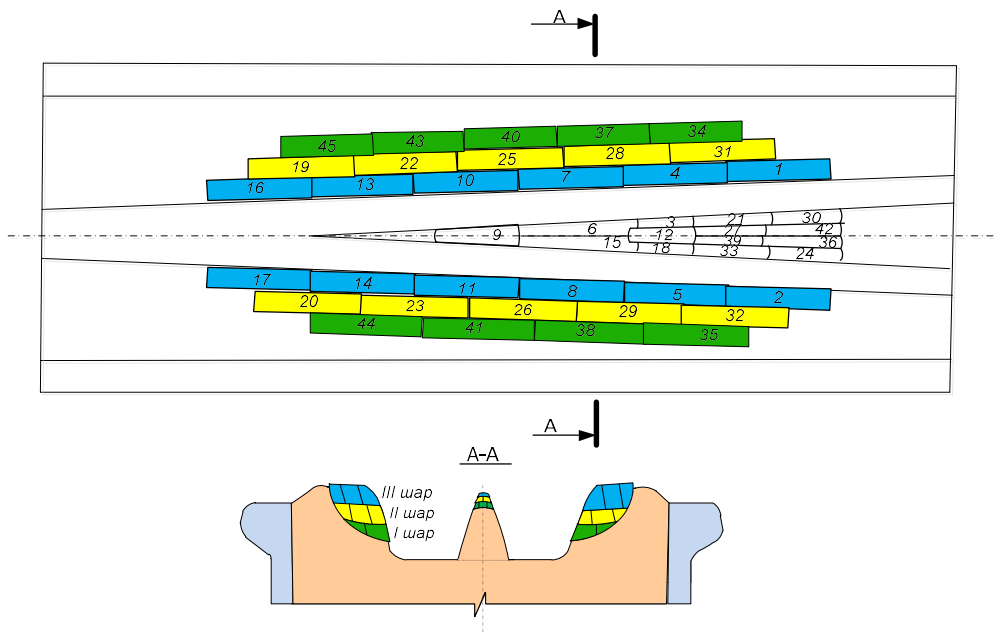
Схема розташування валиків наплавленого металу під час ремонту гострих хрестовин (1-45 - шари наплавлення)
